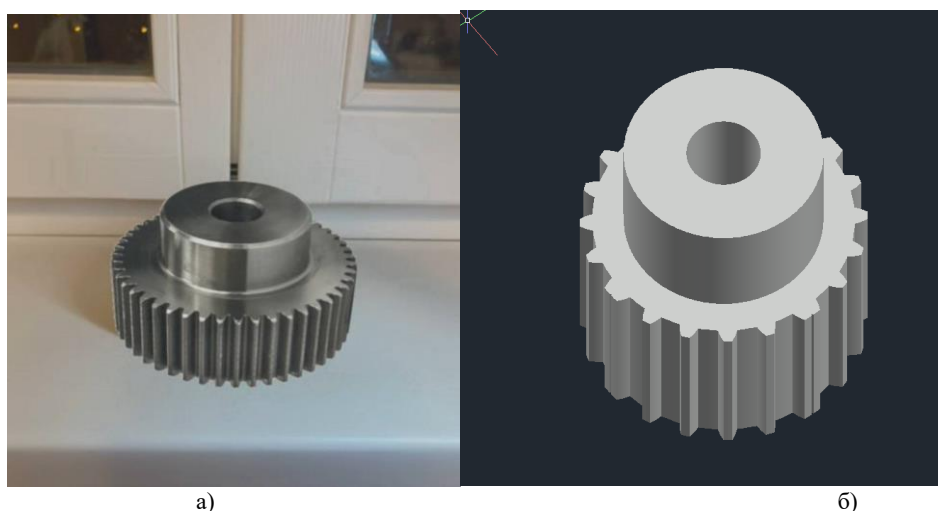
Физический образец шестерни привода масляного насоса автомобиля ГАЗ-24 ранних выпусков (а) и 3D-модель детали, созданная методом обратного инжиниринга (б)
